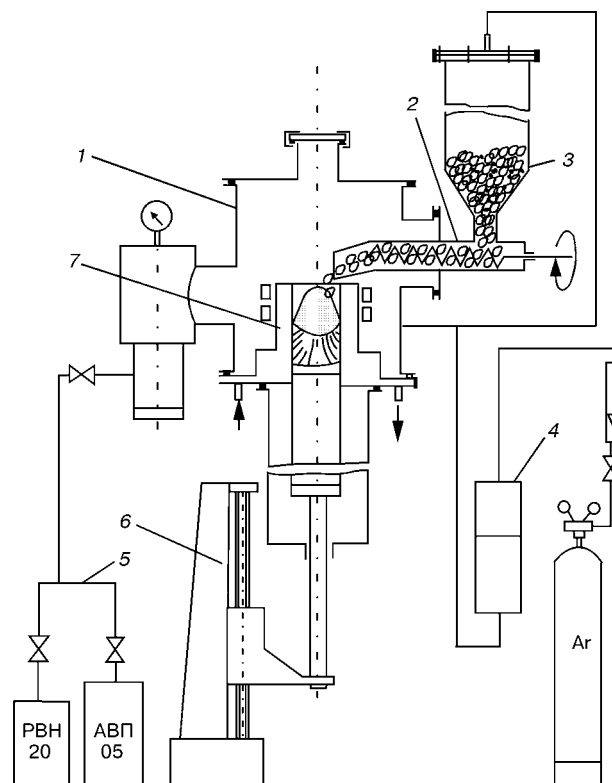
Схема лабораторной установки с секционным кристаллизатором: 1 — вакуумная камера; 2 — шнековый дозатор; 3 — шихтовый бункер; 4 — система газоснабжения; 5 — блок вакуумных насосов; 6 — механизм вытягивания слитка; 7 — кристаллизатор
